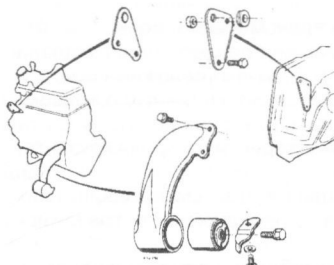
Детали передних креплений двигателя и подъемных скоб (Раздел 6)
